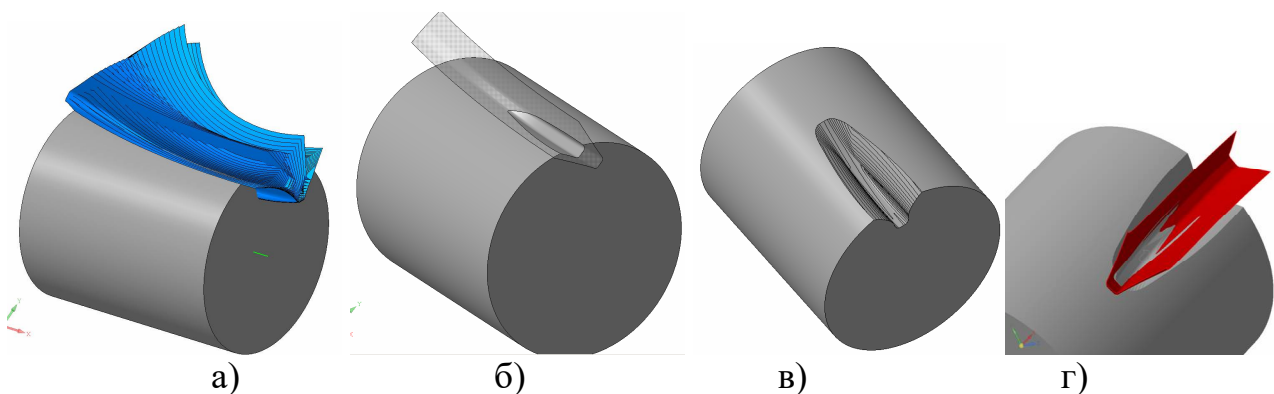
Етапи визначення параметрів зрізаємого шару: а) заготовка з поверхнями різання зубів, б) зрізання шару 1мм зубом фрези, в)результат роботи всіх зубів в западині колеса, г) результат перетину поверхні різання активного зуба з западиною колеса з якої вирізано об'єми шару від роботи попередніхзубів
